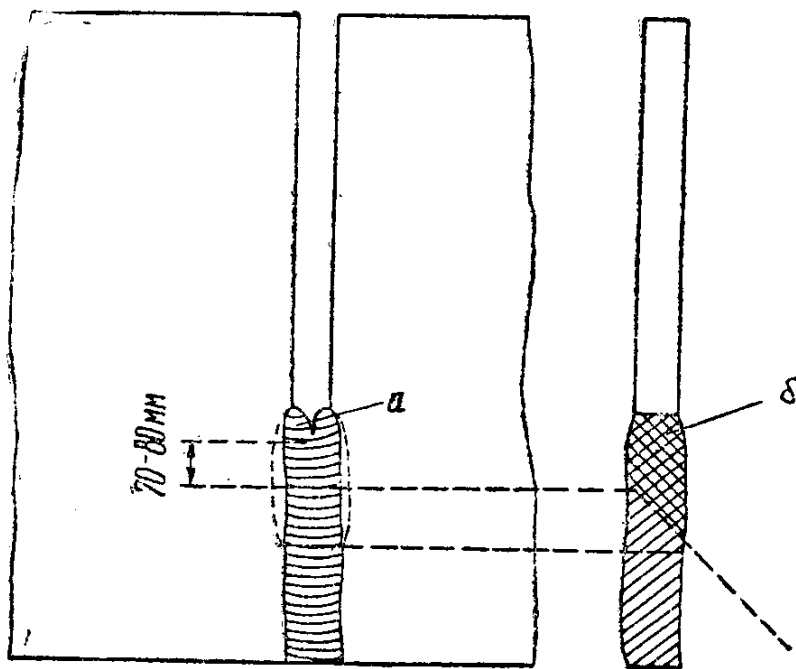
Схема исправления дефектов электрошлакового шва и продолжения сварки после перерыва: а — дефект сварного шва; б — часть сварного шва, подлежащая удалению до продолжения сварки.
